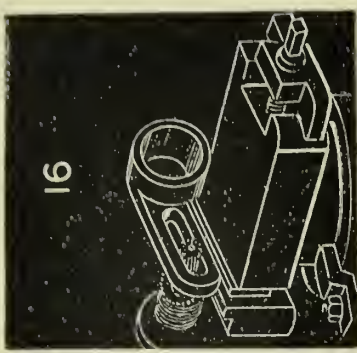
Ausführung verschiedener Fräs-Teil- und Drebearbeiten.
